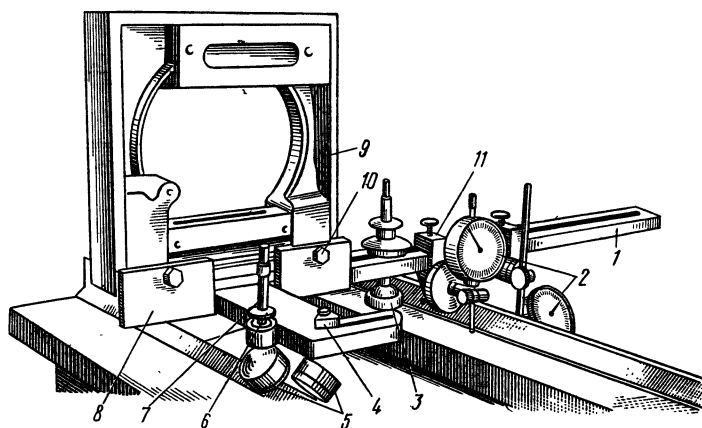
Проверка направляющих станины универсальным приспособлением — мостиком
